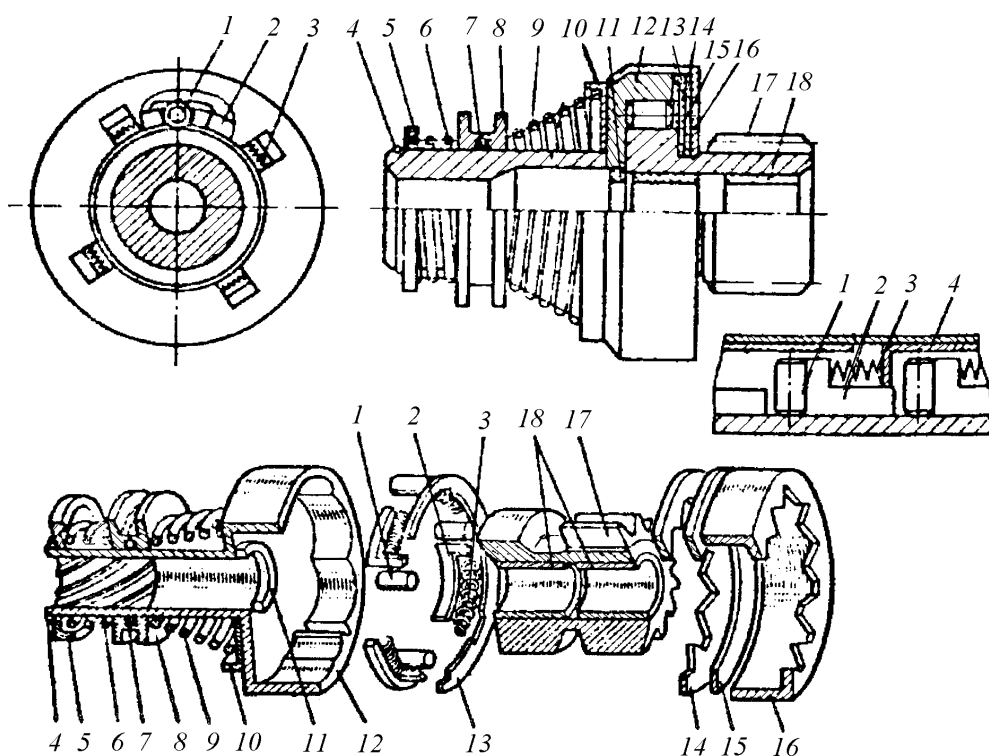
Бесплунжерная четырехроликовая муфта свободного хода и детали приводного механизма:
